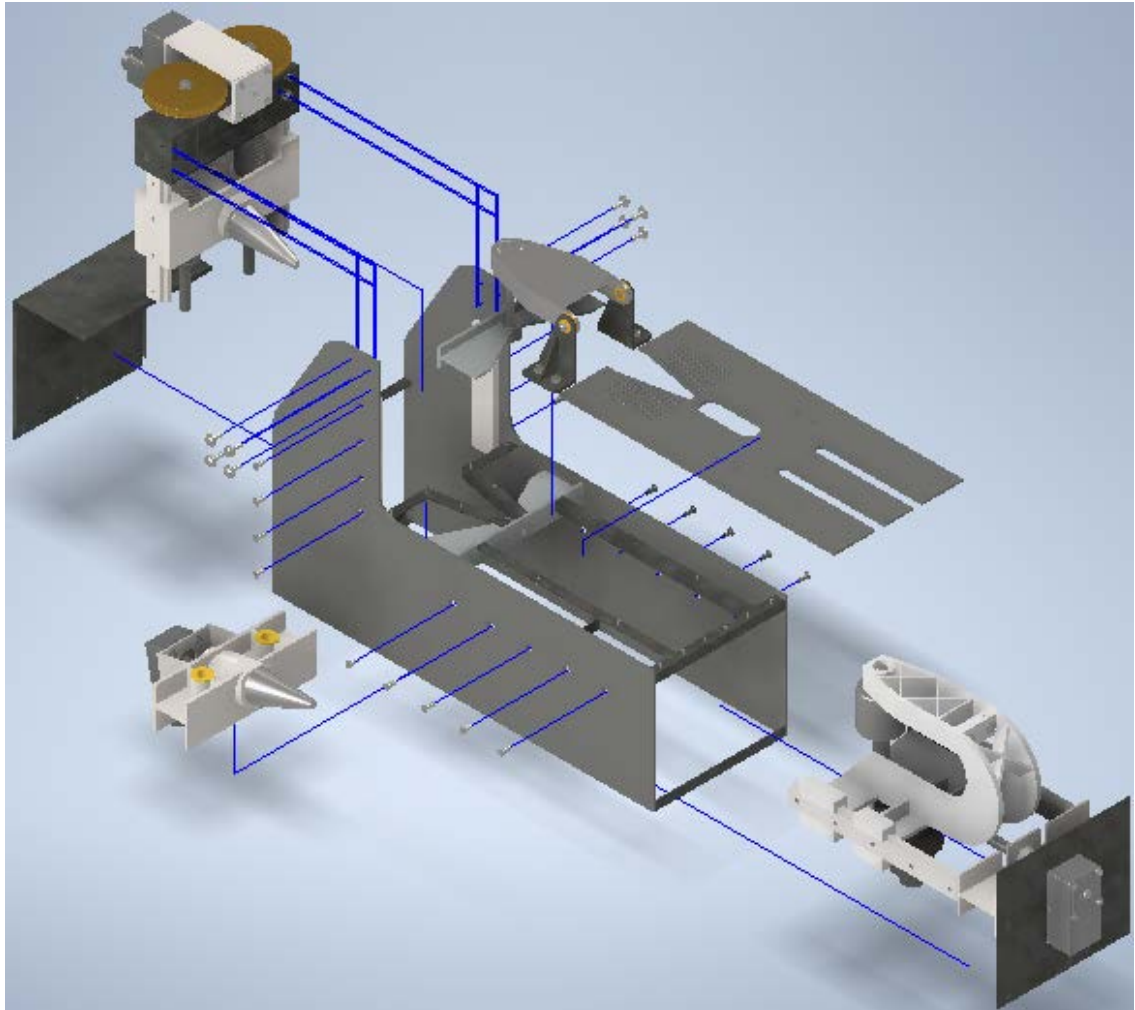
Dibujo de ensamble de sub conjuntos de máquina roladora.
